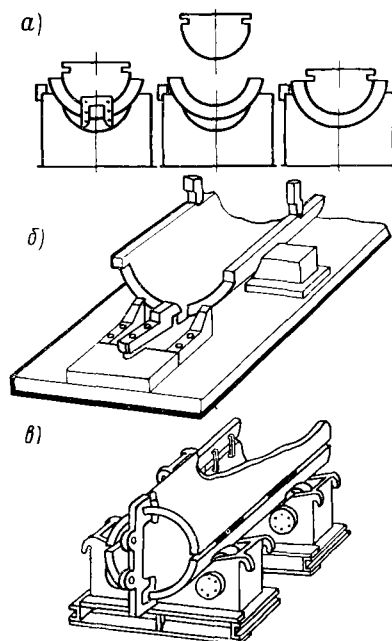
Заготовка элементов и сборка обечайки с двумя продольными стыками
